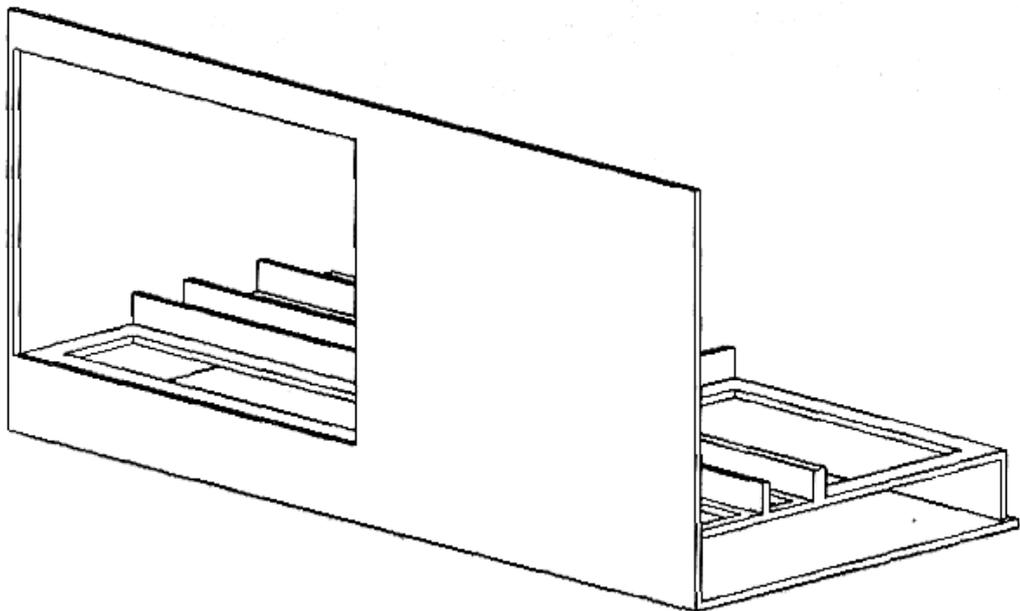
Вариант несущей конструкции для образа 2.2
